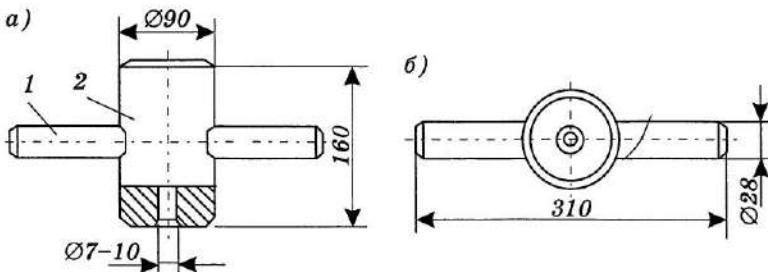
Устройство для забивки и извлечения электродов: а — вид сбоку; б — вид сверху;
